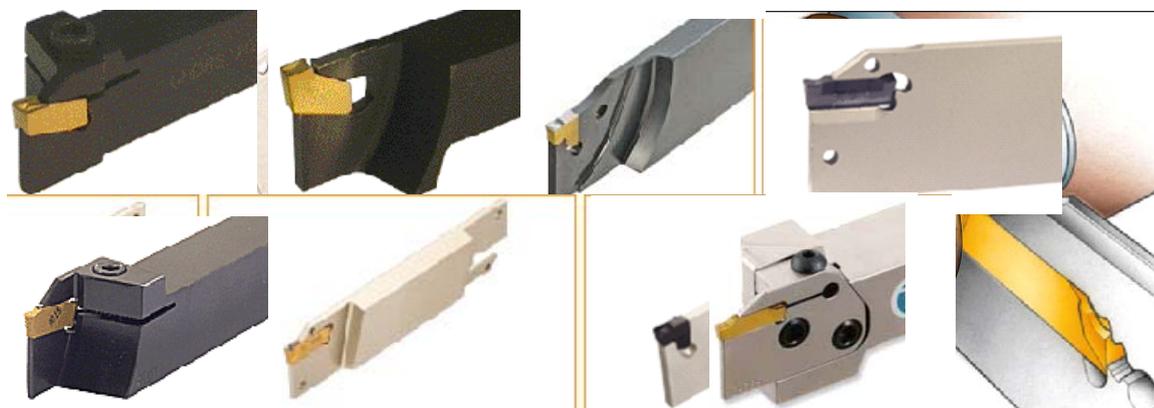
Основные конструкции сборных отрезных резцов с боковой установкой и креплением одно и двугранных неперетачиваемых пластин ведущих мировых фирм
